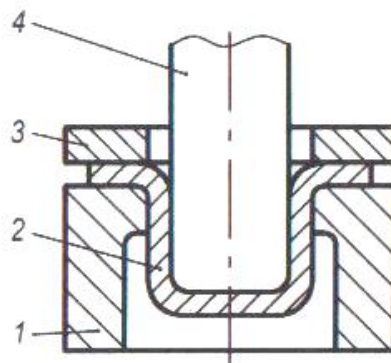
Схема листового штампування (витягування): 1 – матриця; 2 – заготовка; 3 – притискне кільце; 4 – пуансон
